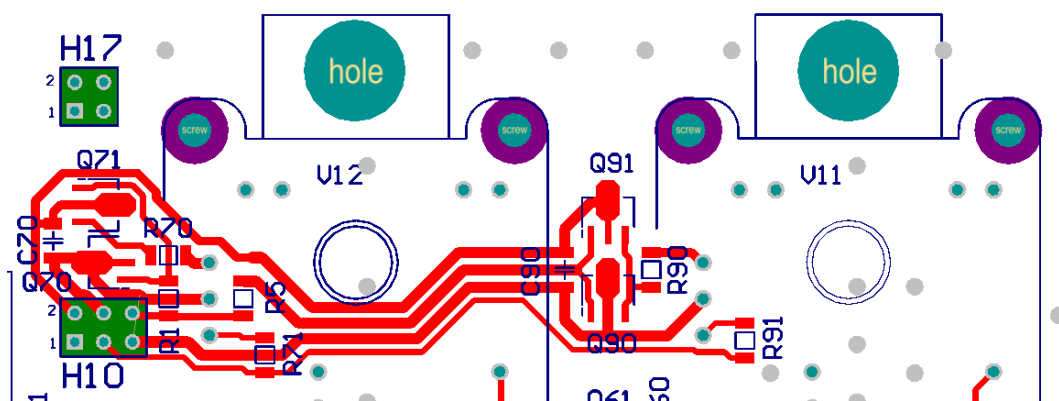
Třetí varianta layoutu měniče 2QC2
